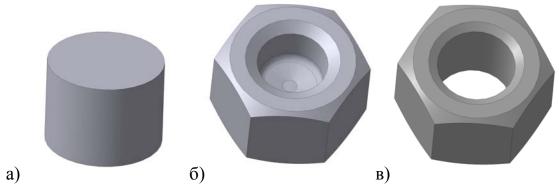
3D модели: а) заготовка; б) поковка гайки; в) гайка
